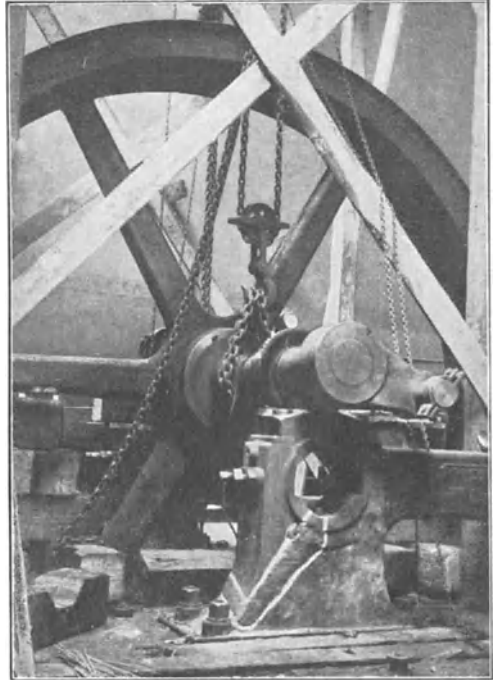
Schweißung eines Kurbelwellenlagers.
